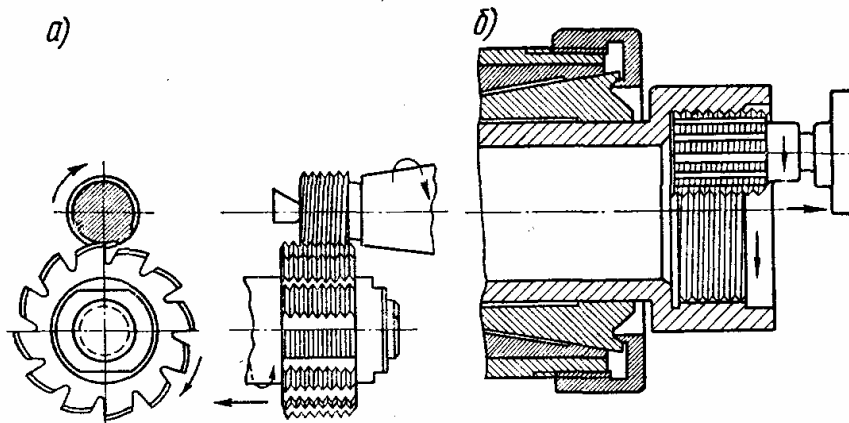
Схемы фрезерования резьбы групповыми фрезами:
